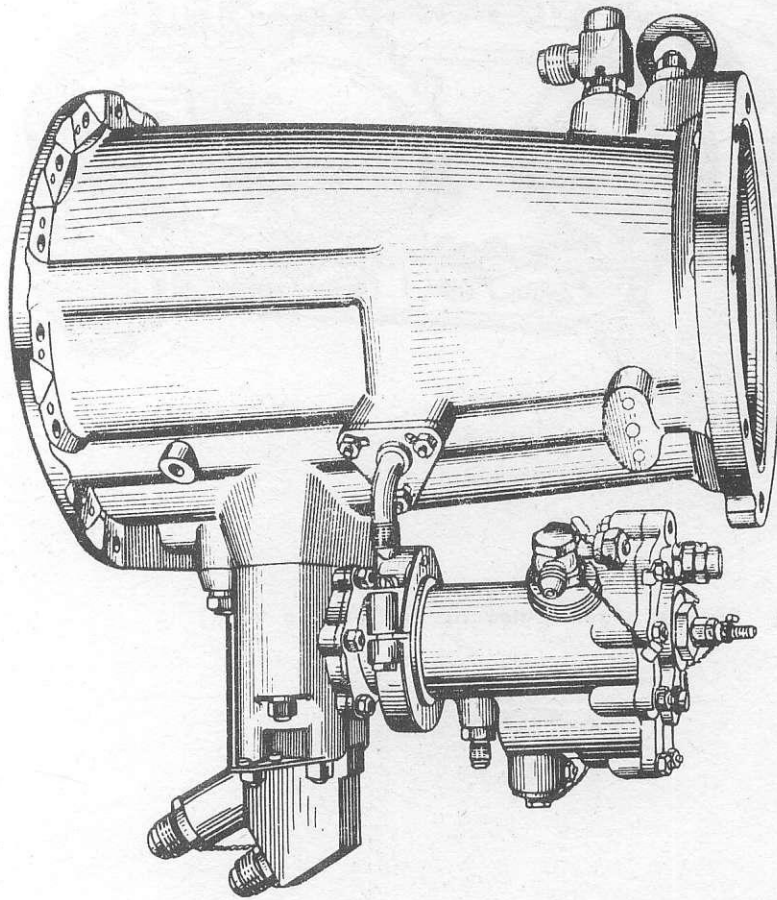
Gehäuse des Hauptantriebes mit dem darauf
